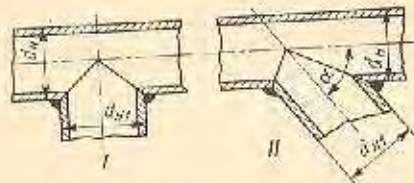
Типовые конструкции сварного подсоединения (врезка) одной трубы к другой под углом:
